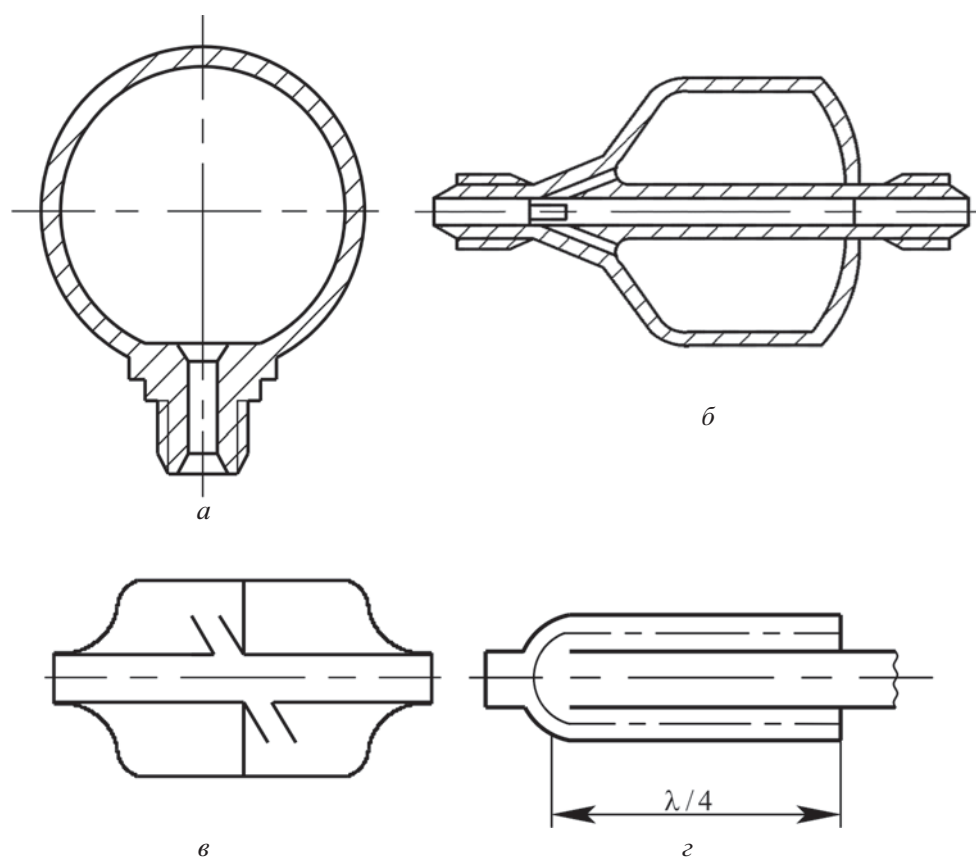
Конструктивные схемы (а, б) и виды (в, г) гасителей типа присоединенного резонатора:
